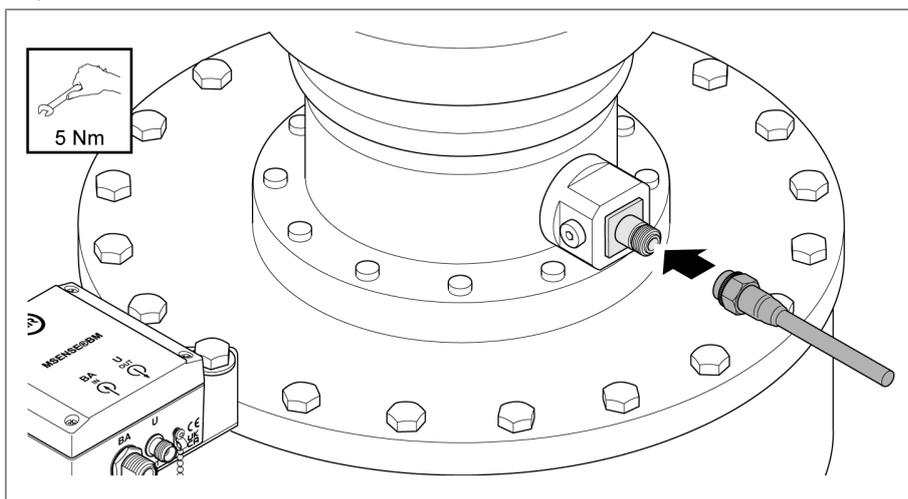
collegare il cavo di collegamento all'adattatore dell'isolatore passante
